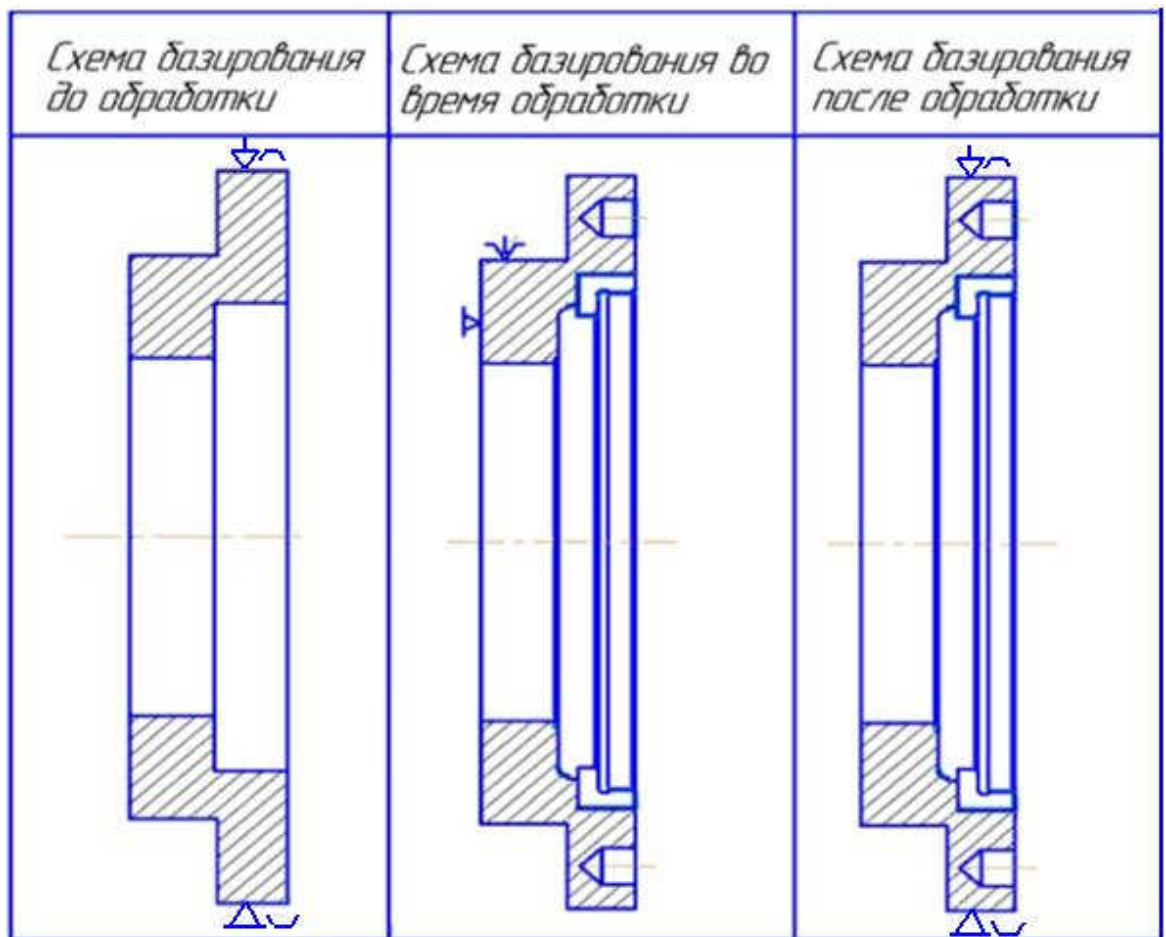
Схема базирования заготовки на 005 комплексной операции с ЧПУ
